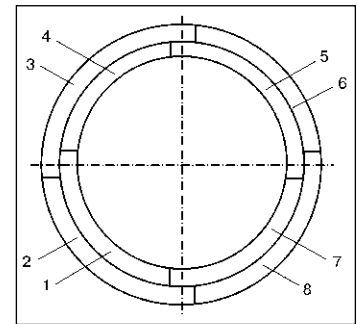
Схема сварки стыка труб с расплавляемой вставкой
